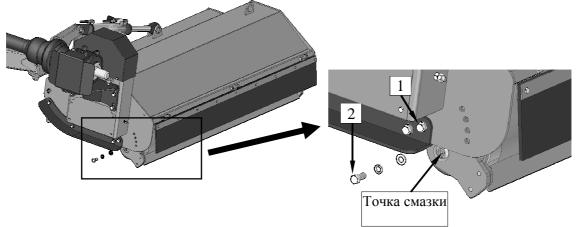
Точка смазки копирующего вала (касатеся KBRP)
